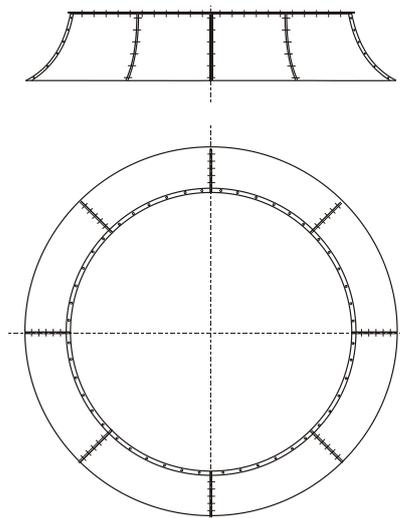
Чертеж коллектора плавного входа ГАЦ-5-КПВ
